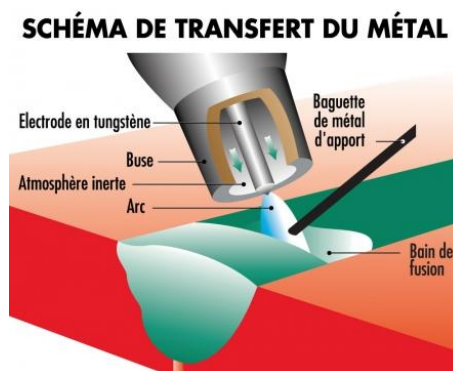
Soudure au TIG (Tungstène Inert Gas)
